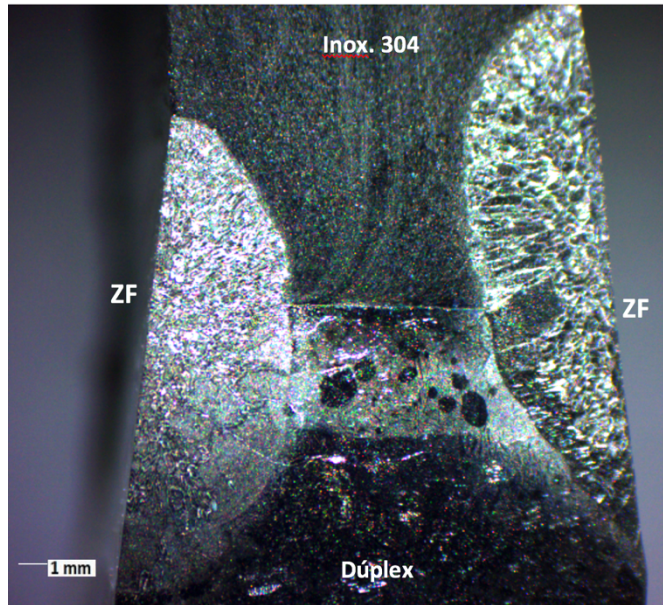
Soldadura disímil realizada a 100 A, vista en microscopio estereográfico. (ZF=zona de fusión)
